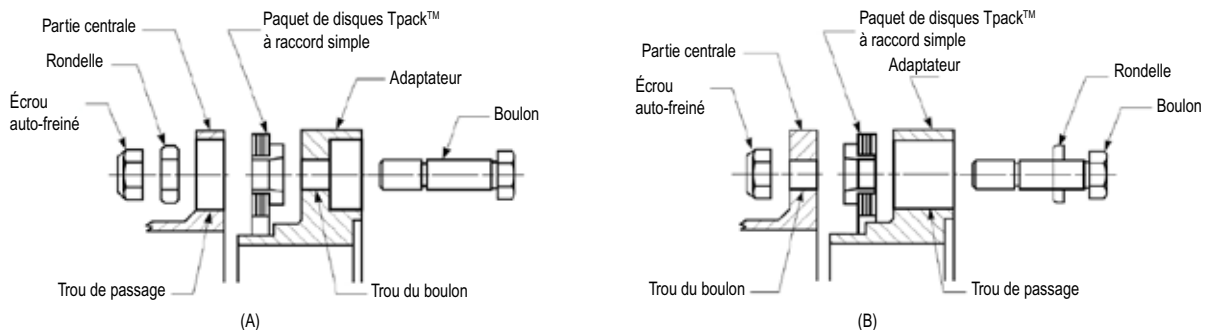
Paquet de disques Tpack assemblé avec l'adaptateur
